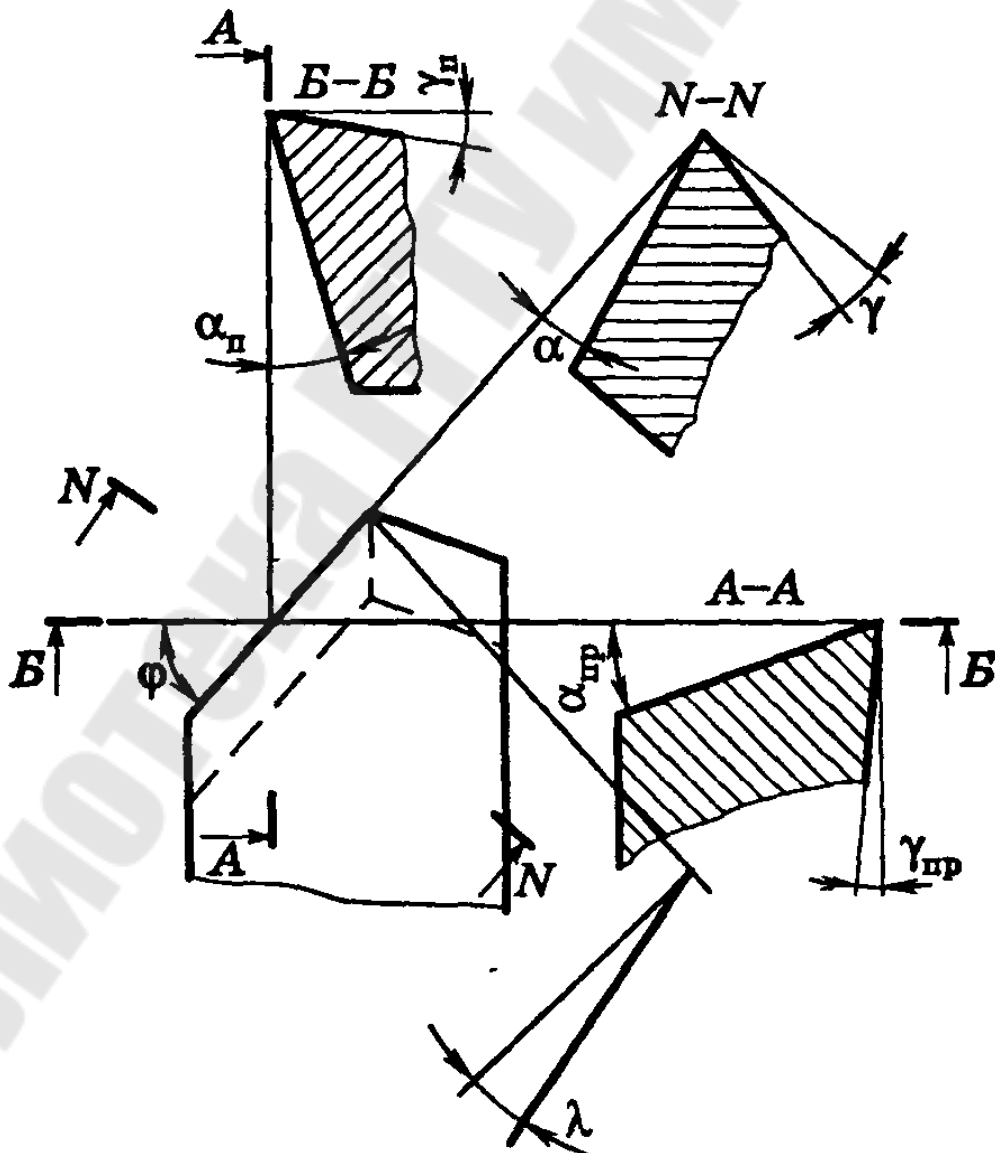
Углы лезвия инструмента токарного резца
